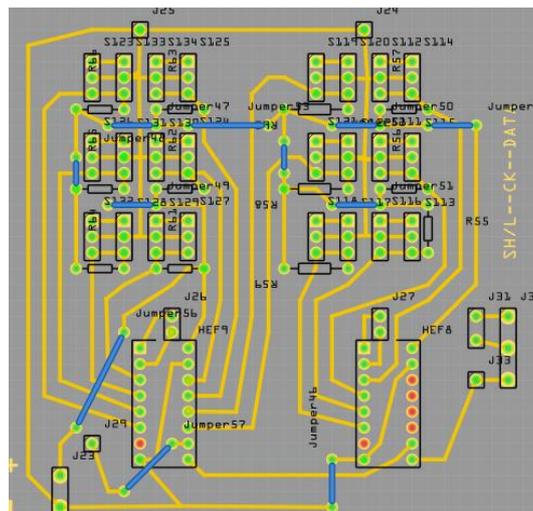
Diseño PCB del módulo de escritura-segunda tarjeta
